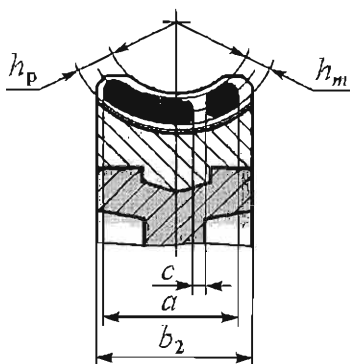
Суммарное пятно контакта на рабочей поверхности зуба червячного колеса
